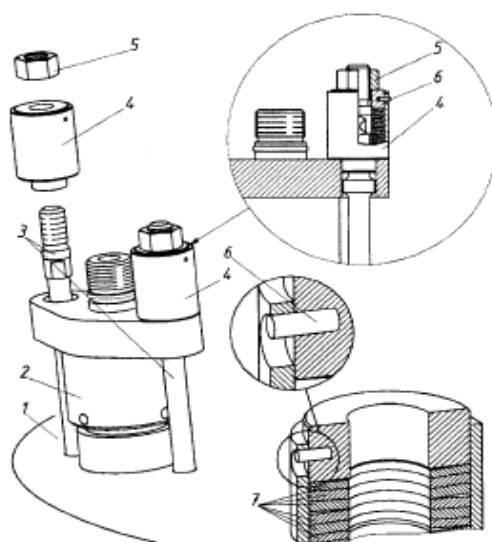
Пружний амортизатор нормування величини затягування форсунки (двигуни серії МС і МЕ фірми MAN) : 1 – кришка циліндра; 2 – форсунка; 3 – шпильки кріплення форсунки; 4 – пружний амортизатор; 5 – гайка кріплення форсунки; 6 – контрольний штифт; 7 – набір тарілчастих пружин
